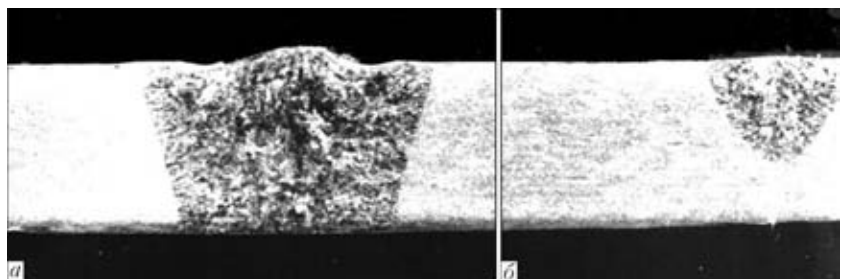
Макроструктуры наплавки на титановом сплаве ВТ1 ($\delta = 10$ мм): а — лазерно-дуговая сварка; б — лазерная сварка
